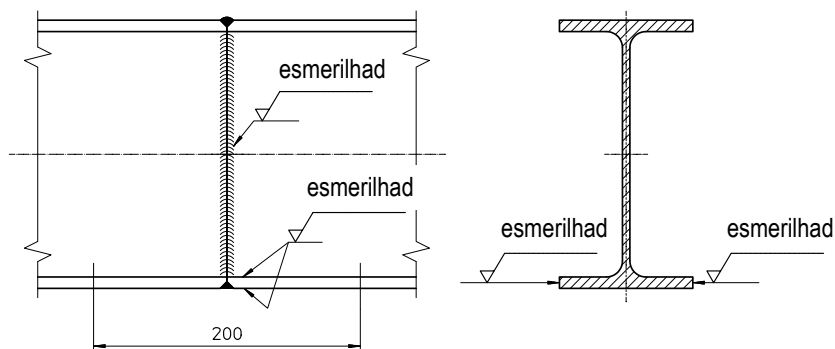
Alisamento de vigas-trilho soldadas
